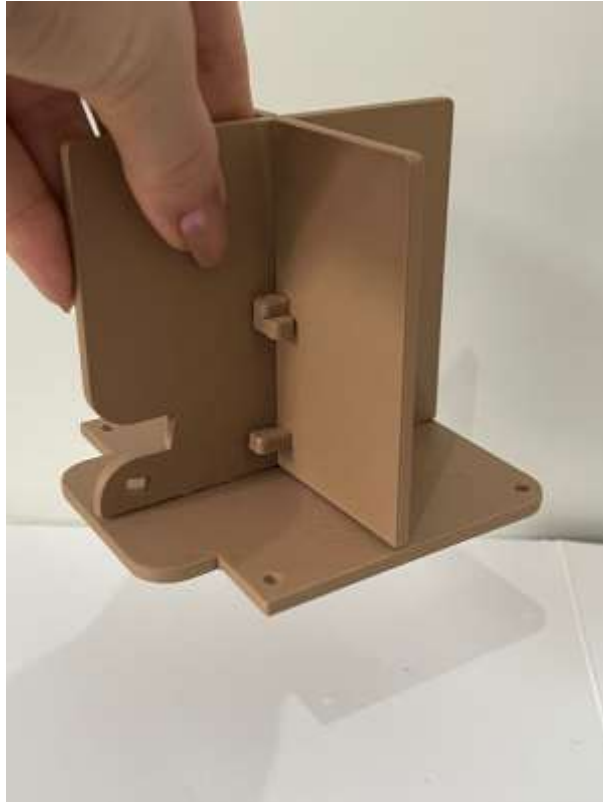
Teste de fixação e encaixe da peça "C" na estrutura de suporte (Fonte: o autor)
